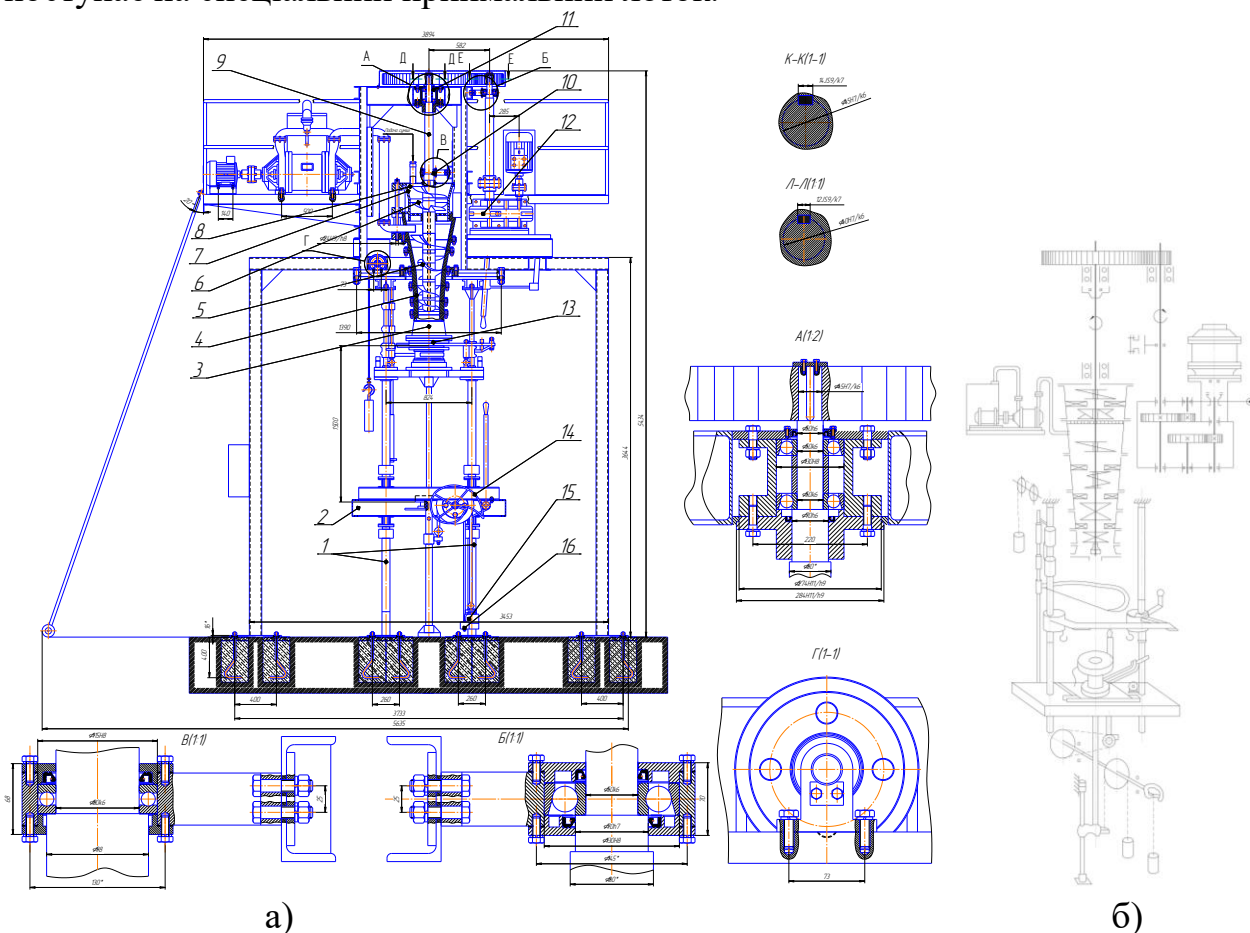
Вертикальний вакуум-прес для формування раструбних каналізаційних труб а) вид загальний; б) кінематична схема
